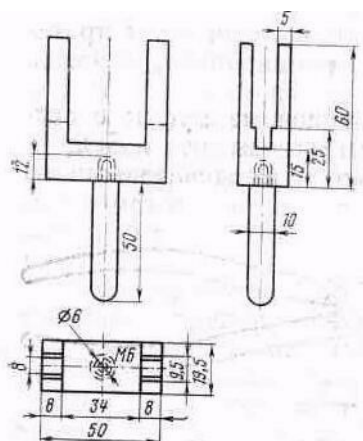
Шаблон проверки совпадения средней плоскости червячного колеса с осью червяка в редукторе КПТ
